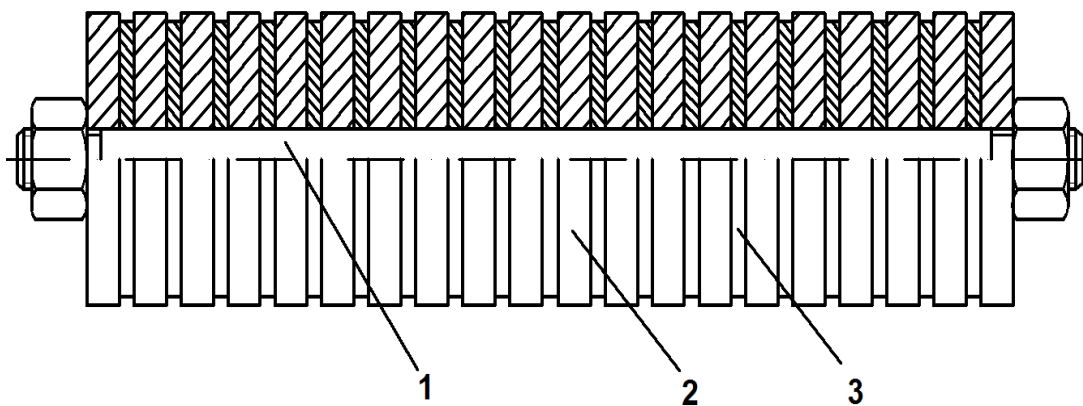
Оправка в сборе с деталями, которые подвергаются терморихтовке до применения абразивной обработки затопленными струями: 1 – шпилька; 2 – жесткие шайбы; 3 – детали для терморихтовки
